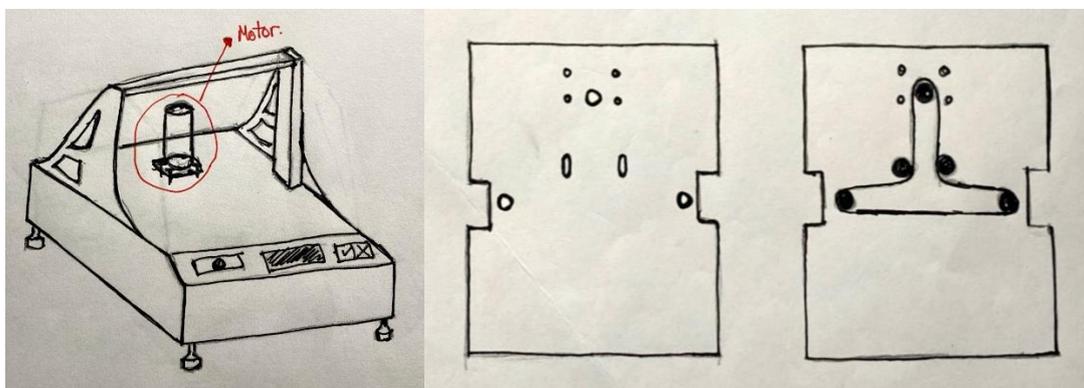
Dibujo posicionamiento motor y taladros/ranuras de motor y poleas.
